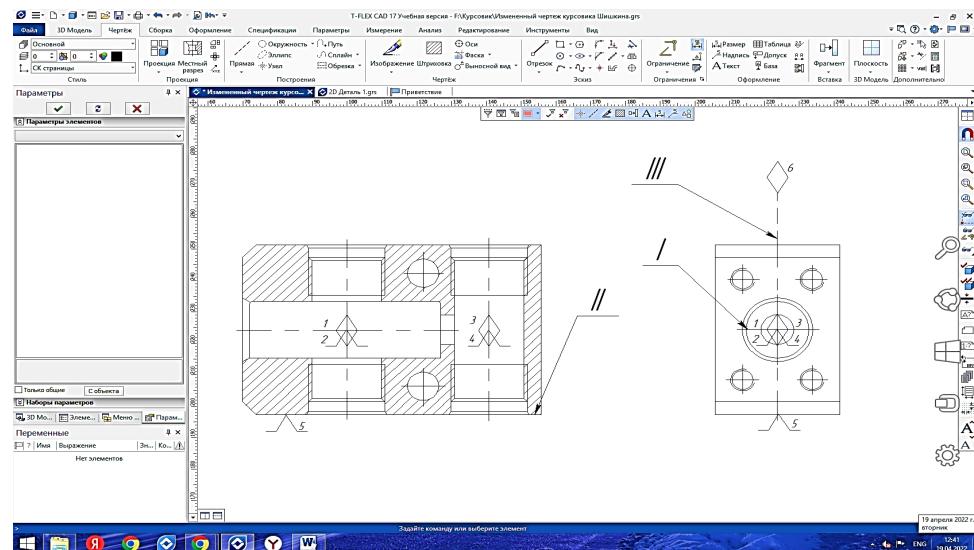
Схема сил закрепления заготовки детали ПЛИТА в тисках с призматическим губками (Переход 6)
